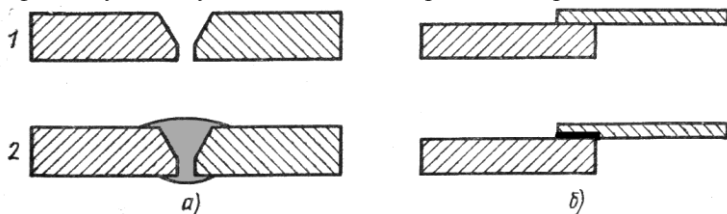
Схема пайки-сварки (а) и сварки-пайки (б)
